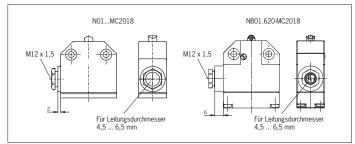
Maßzeichnung N01...MC2018/NB01.620-MC2018 mit Halbverschraubung
